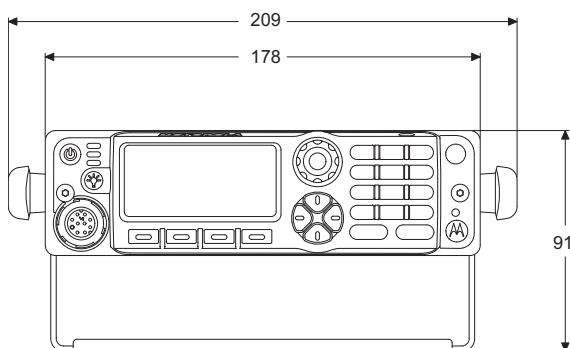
Vista Frontal da Cabeça de Controle O7 com Munhão e Montagem Remota
